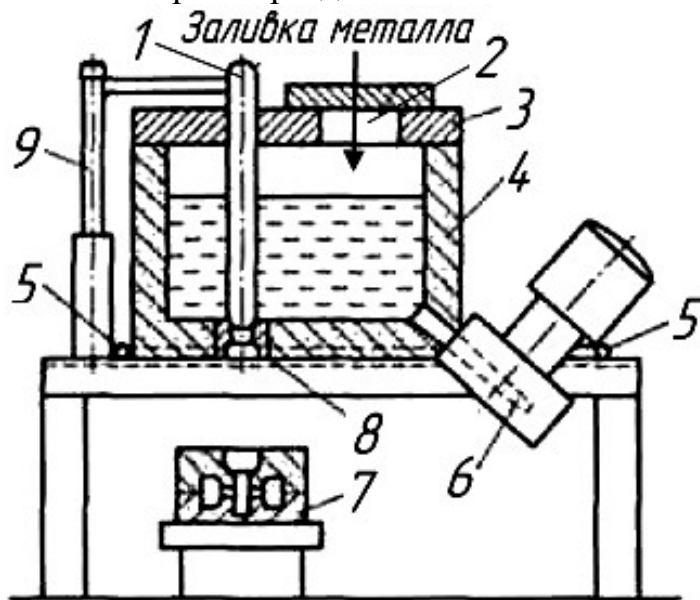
Схема заливочной установки «Поуромат»: 1 — стопор; 2 — окно для заливки жидкого металла; 3 — крышка печи; 4 — раздаточная печь; 5 — тележка для перемещения ЗУ перпендикулярно литейному конвейеру; 6 — индуктор; 7 — литейная форма; 8 — керамическая втулка; 9 — механизм открывания стопора
